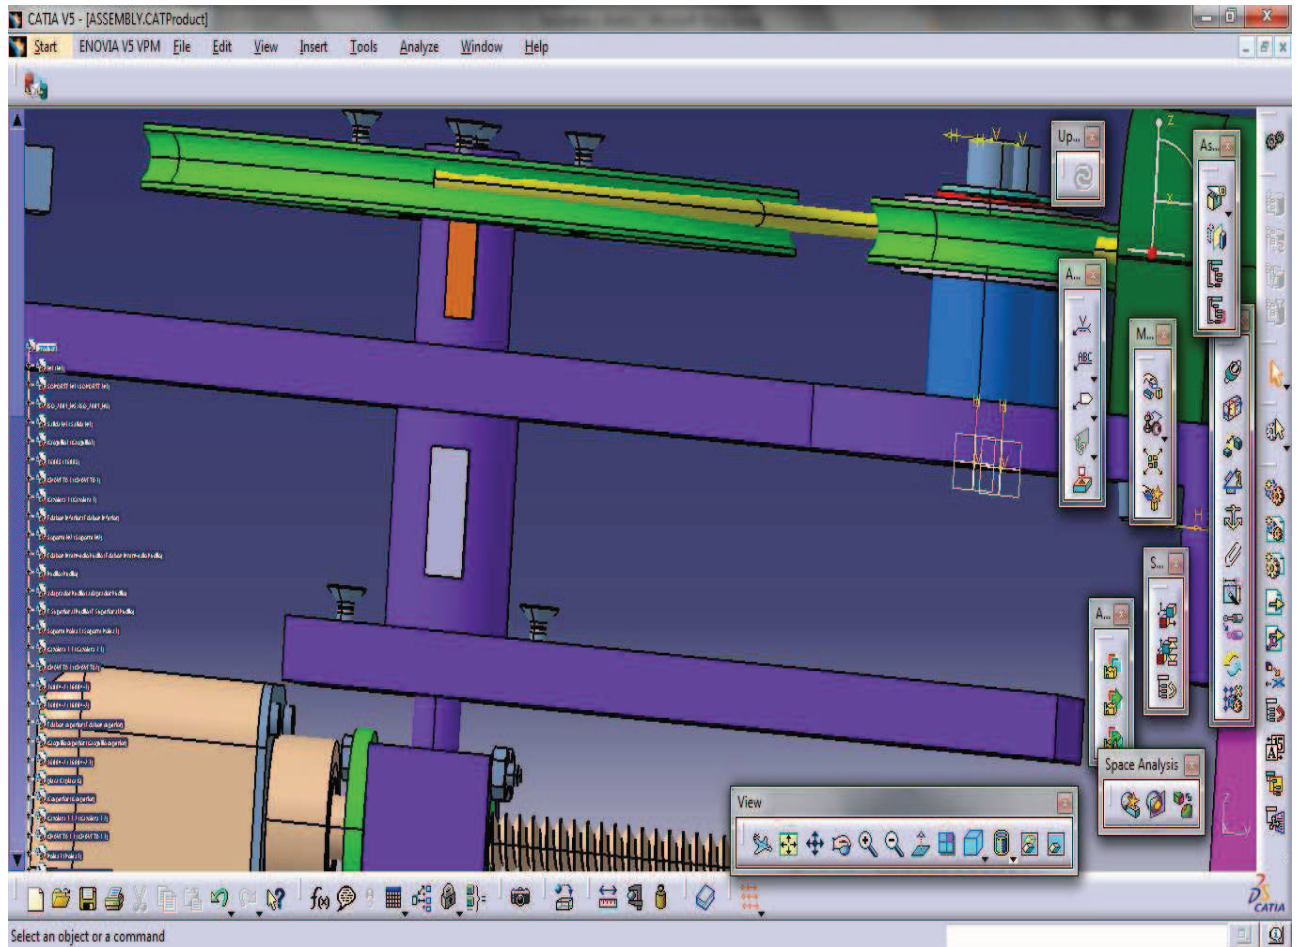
Vista del soporte de la polea principal dentro del ensamblaje.
